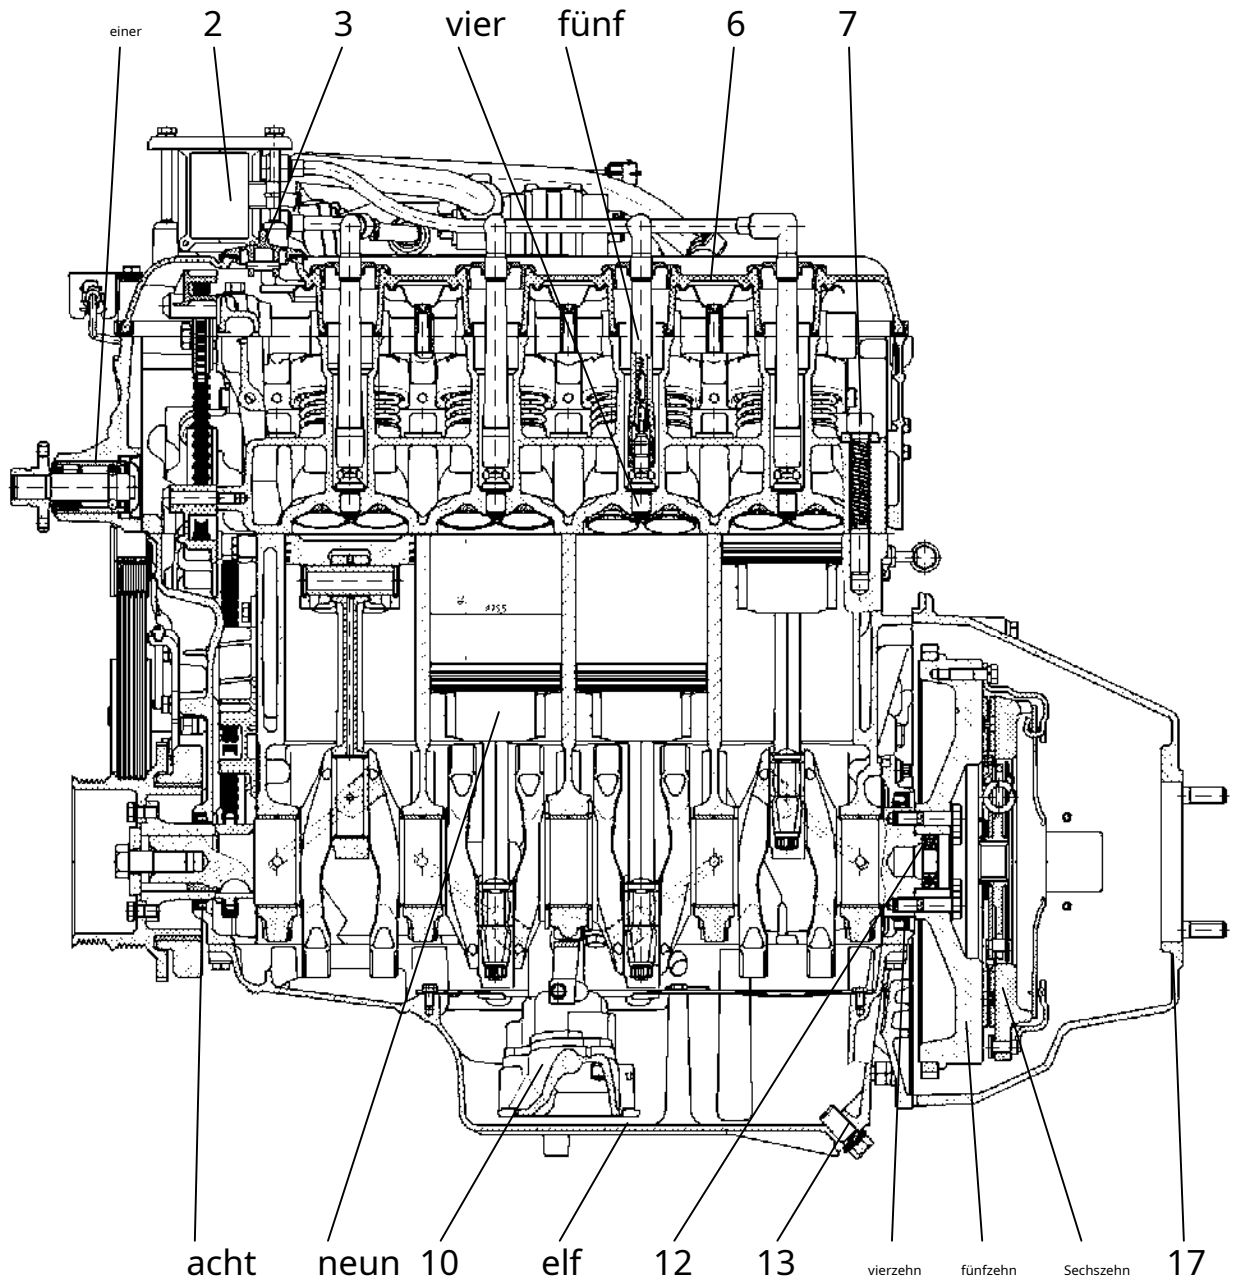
Längsschnitt des Motors mit Halterung der Servolenkungspumpe:
